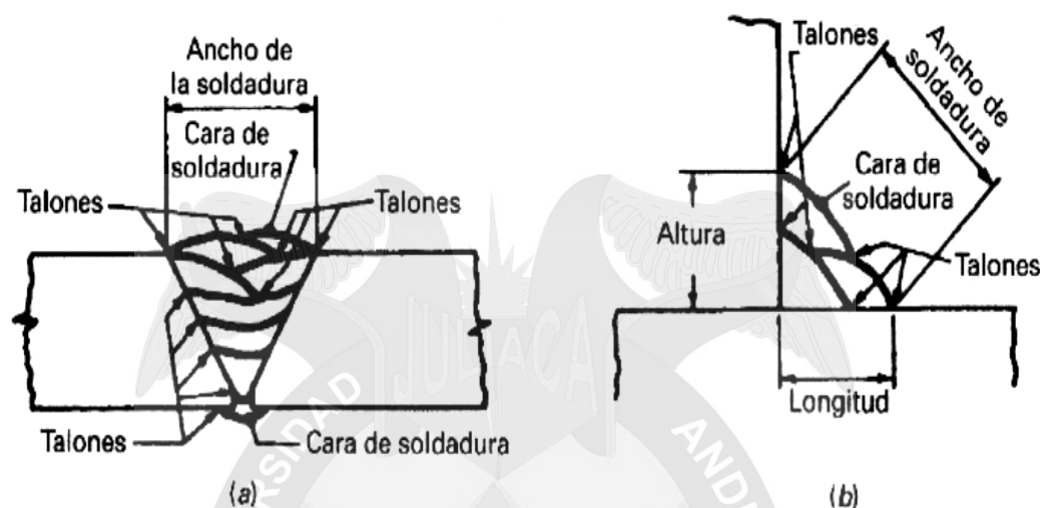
Terminología de la soldadura para soldadura a tope y con material de relleno.
